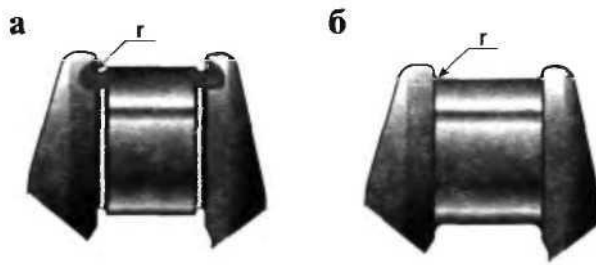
Вигляд геометричних форм галтелей шийок колінчатого вала: а – стандартної конструкції; б - для високофорсованих двигунів;  $r$  – радіус заокруглення
